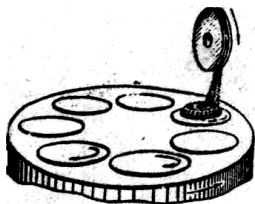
Схема обработки конических зубчатых колес на дробеструйной установке с вращающимся столом
